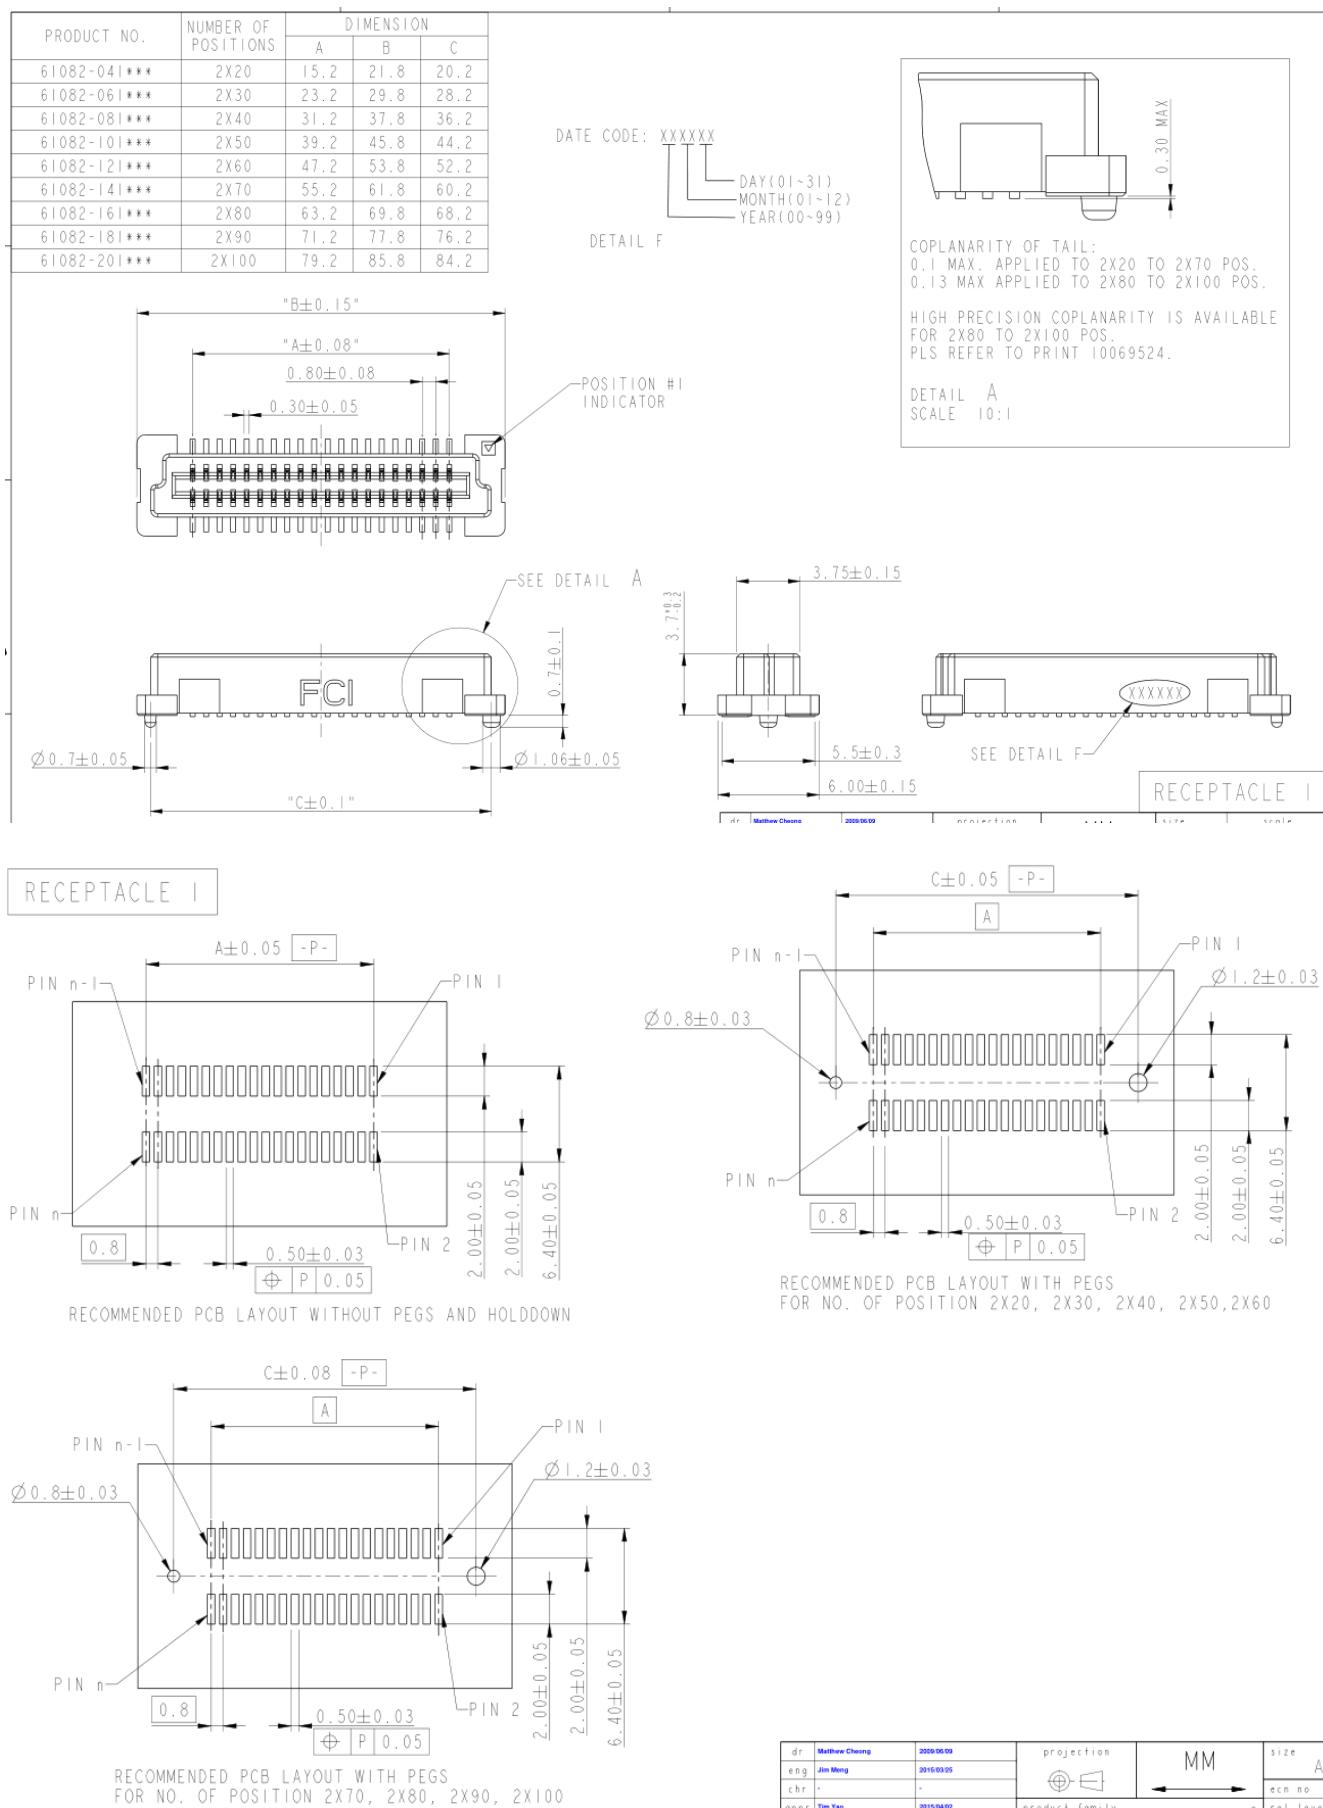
间距 0.8mm 立式双排 40 PIN PCB 封装
